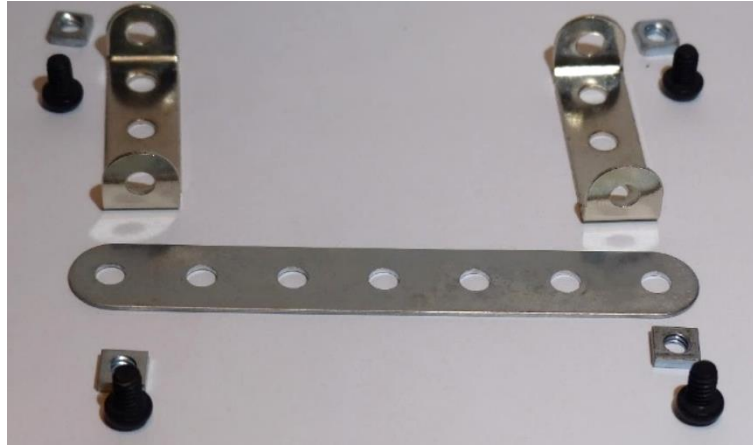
1 platter Metallstab mit 7 Löchern, 2 platte und beidseitig angewinkelte Metallstäbe mit 5 Löchern, 4 schwarze Schrauben und 4 Schraubenmuttern aus Metall
